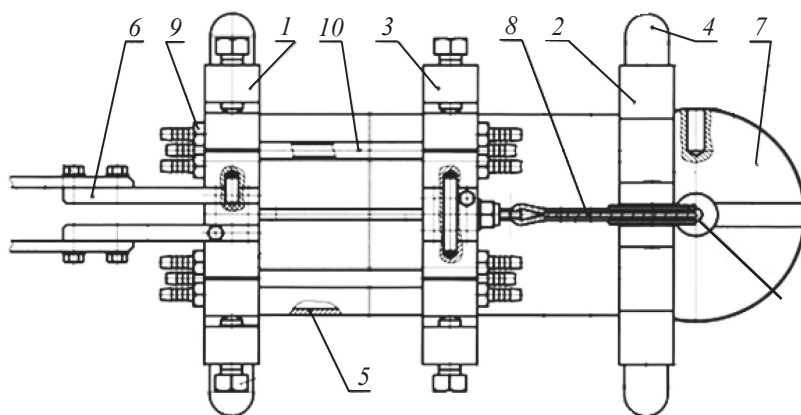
Общий вид (вид сверху) установки электроконтактного нагрева труб с растяжением:
